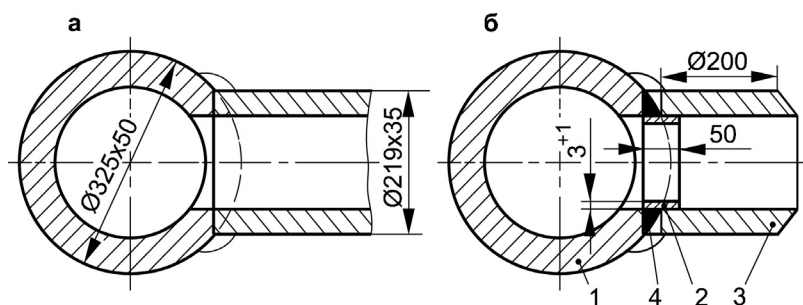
Изменение конструкции узла приварки гйба к стакану:
